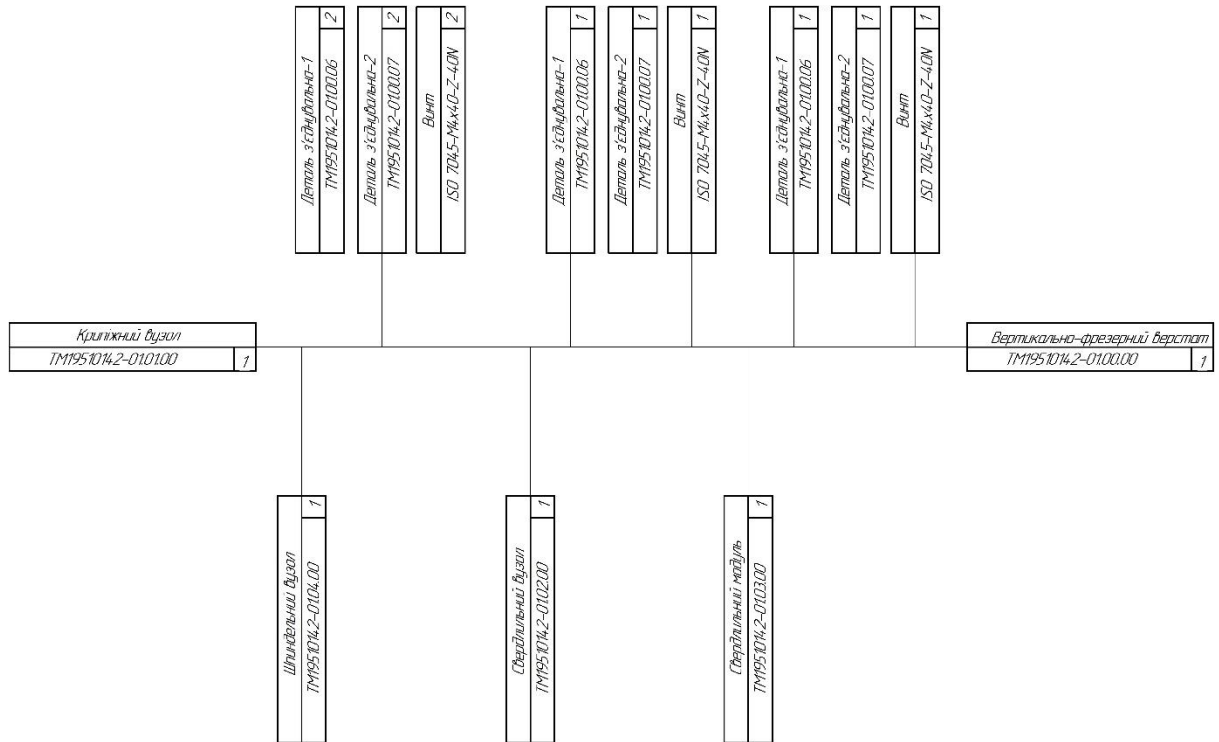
Схема складання вертикально-фрезерного модуля
